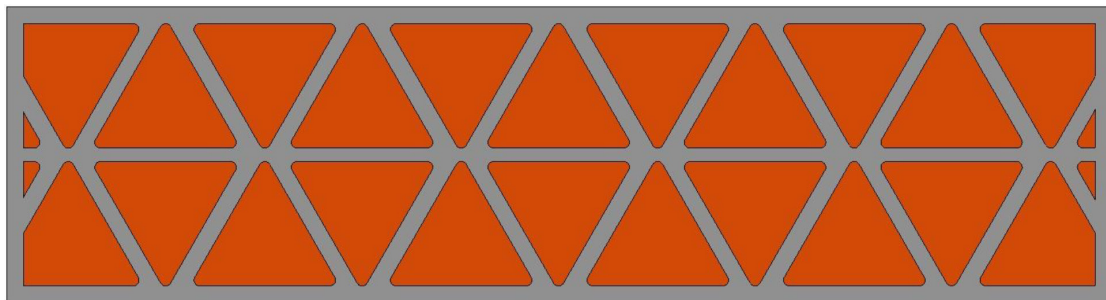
Зміна розташування одиничних плям покриття однакової форми на оброблюваній поверхні заготовки
